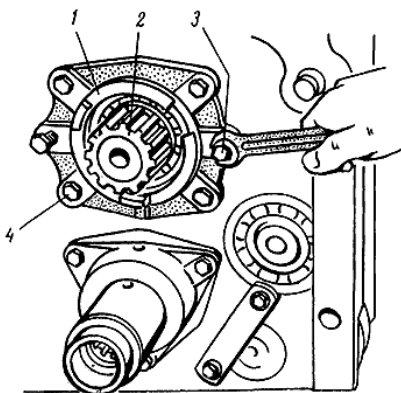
Выпрессовка стакана первичного вала: 1 — стакан первичного вала; 2 — первичный вал; 3 — технологический болт; 4 — болт
